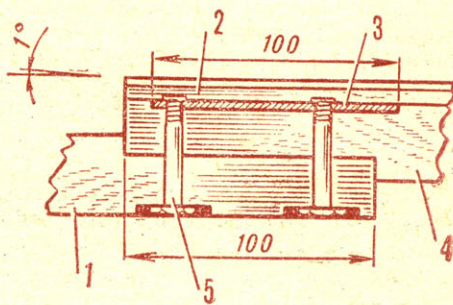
Крепление грифа к корпусу гитары: 1 — корпус; 2 — накладка; 3 — стальная жесткая пластина; 4 — гриф; 5 — стяжные болты.
